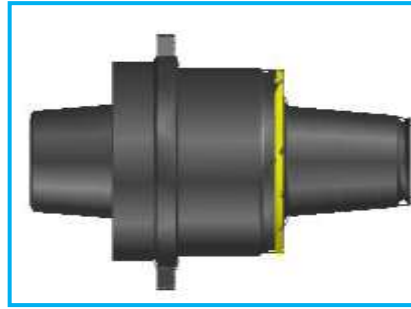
BOQUILLA TIPO INSERTO. FUENTE [6]
